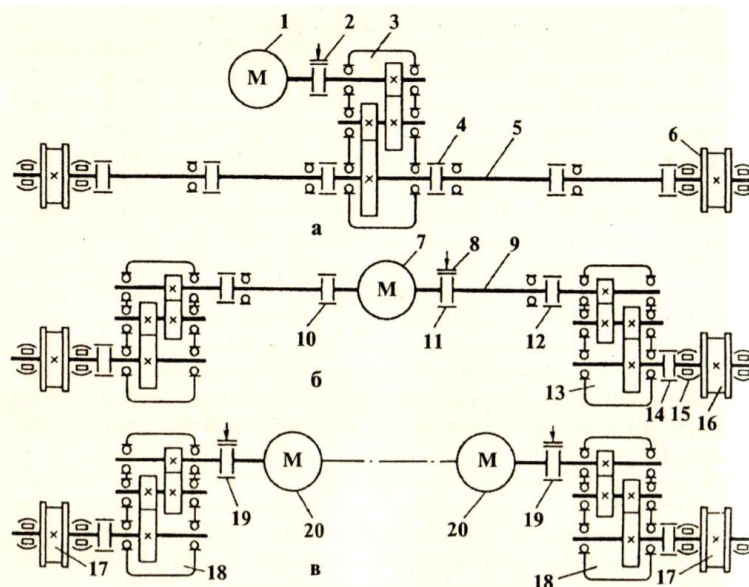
Кинематические схемы механизмов передвижения:
